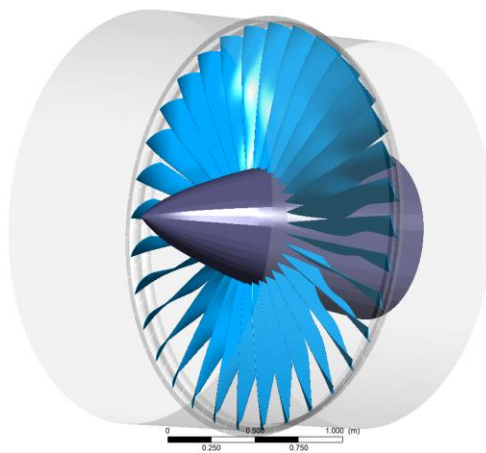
Ізометричний вид моделі робочого колеса вентилятора з надроторним пристроєм
